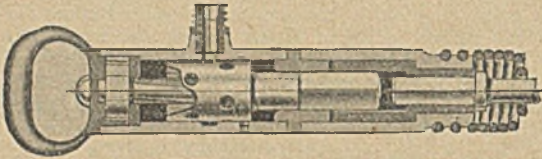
Werkzeug zum Entkernen von Granaten.
